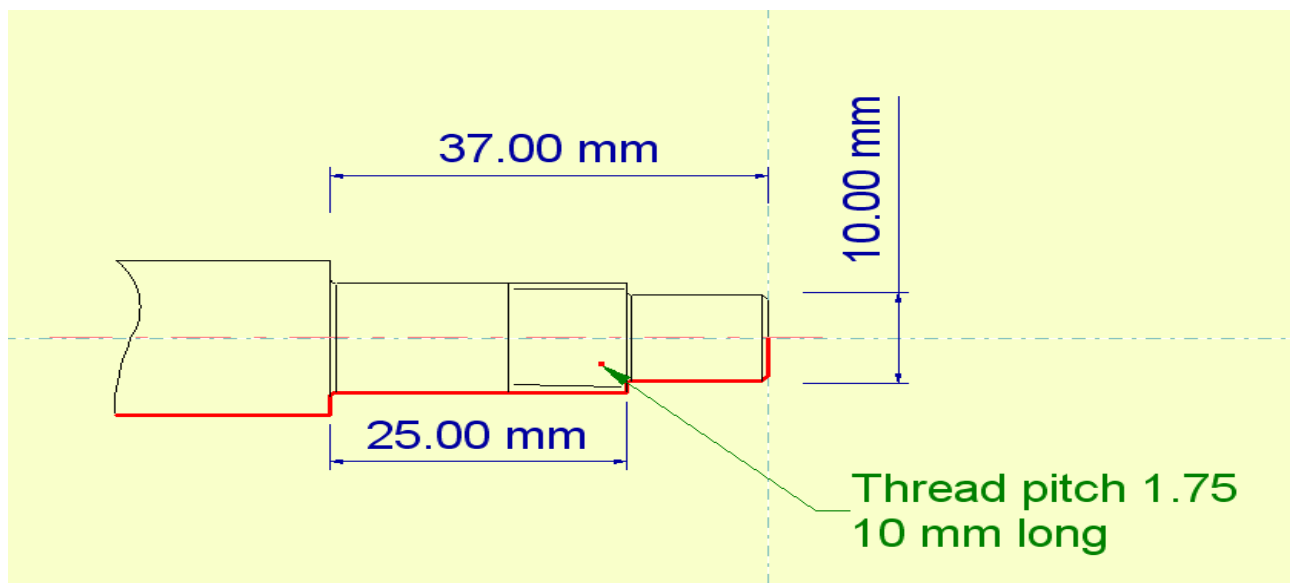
Уступчатый конец вала с размерами для ручной токарной обработки
